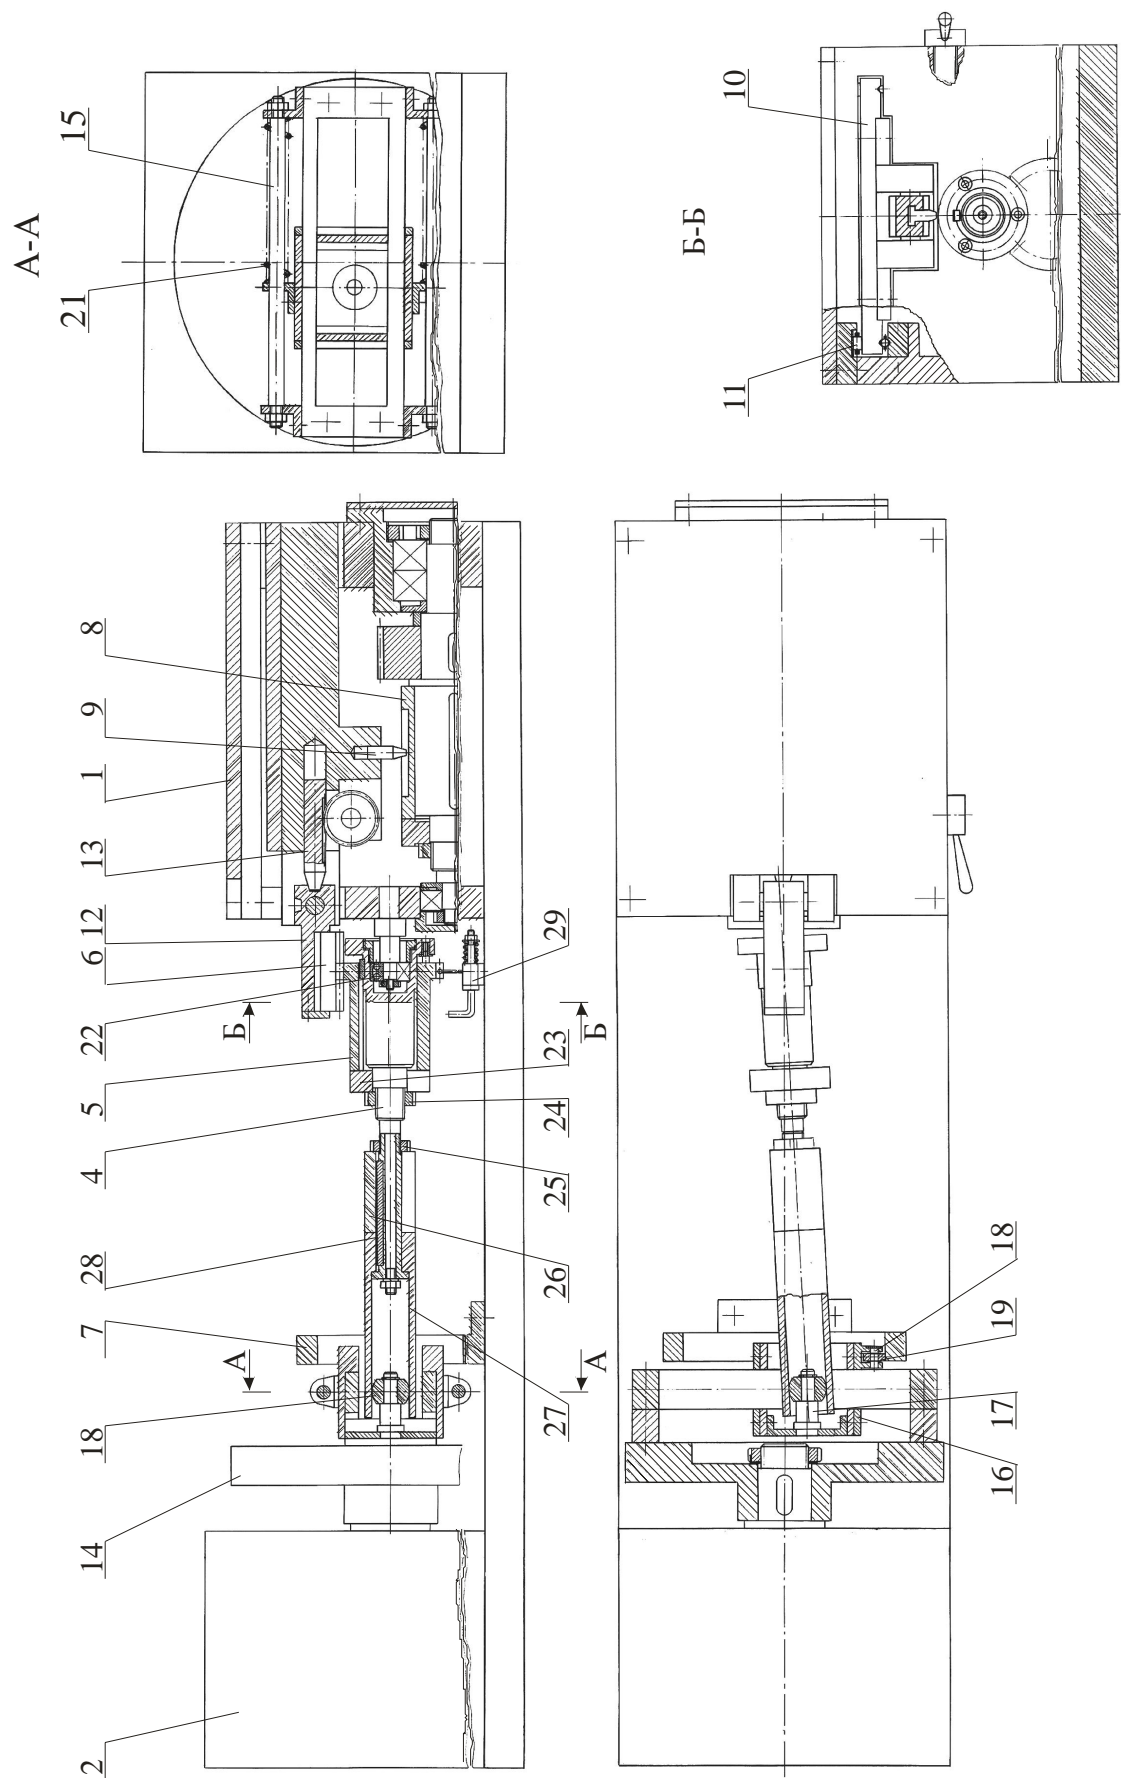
Общий вид устройства для чистовой обработки зубьев с пространственной геометрией
